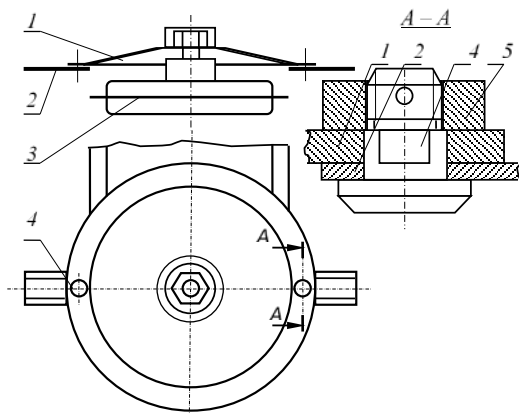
Схема ротора с шарнирно закрепленными на диске ножами: 1 – диск; 2 – ножи; 3 – привод; 4 – соединительные пальцы; 5 – гайка
